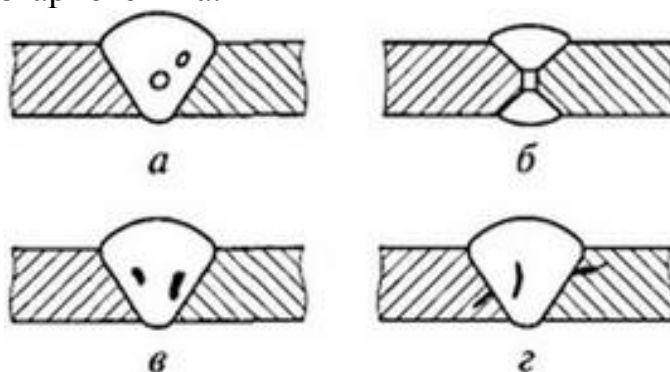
Внутрішні дефекти зварного шва:
